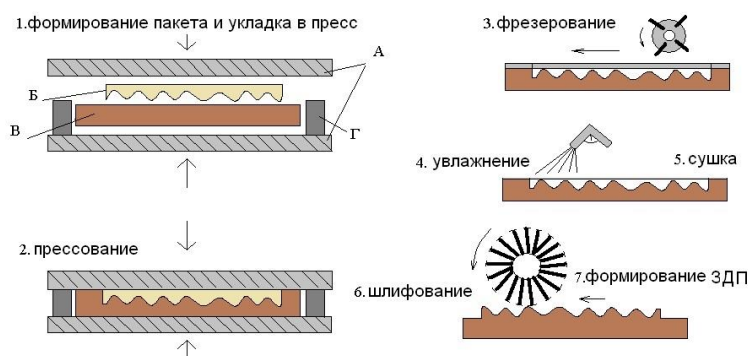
Технологический процесс декорирования поверхности детали или заготовки из древесины: А – плиты пресса; Б – пуансон; В – заготовленная деталь древесины; Г – планки
